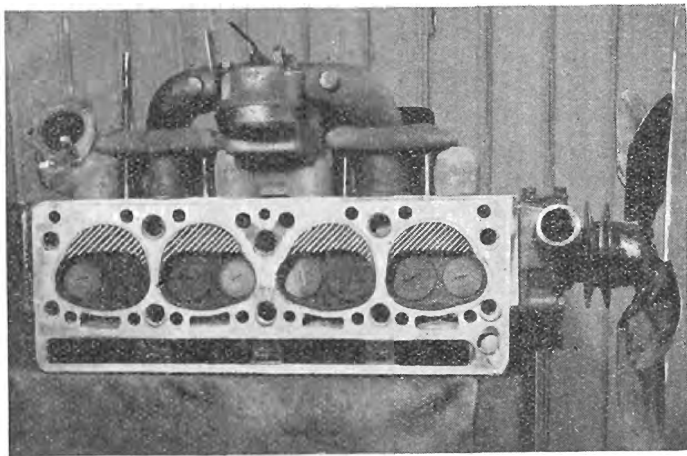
Chambres d'explosion de la culasse 402. (Après chaque réalésage il y aura lieu de fraiser la partie hachurée en vue de conserver le taux de compression d'origine.)
